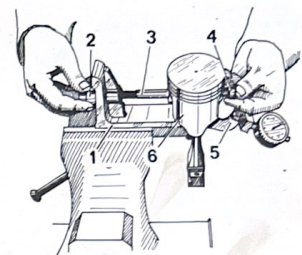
Montaje del conjunto biela-bulón-pistón para la prueba de carga axial del bulón.
